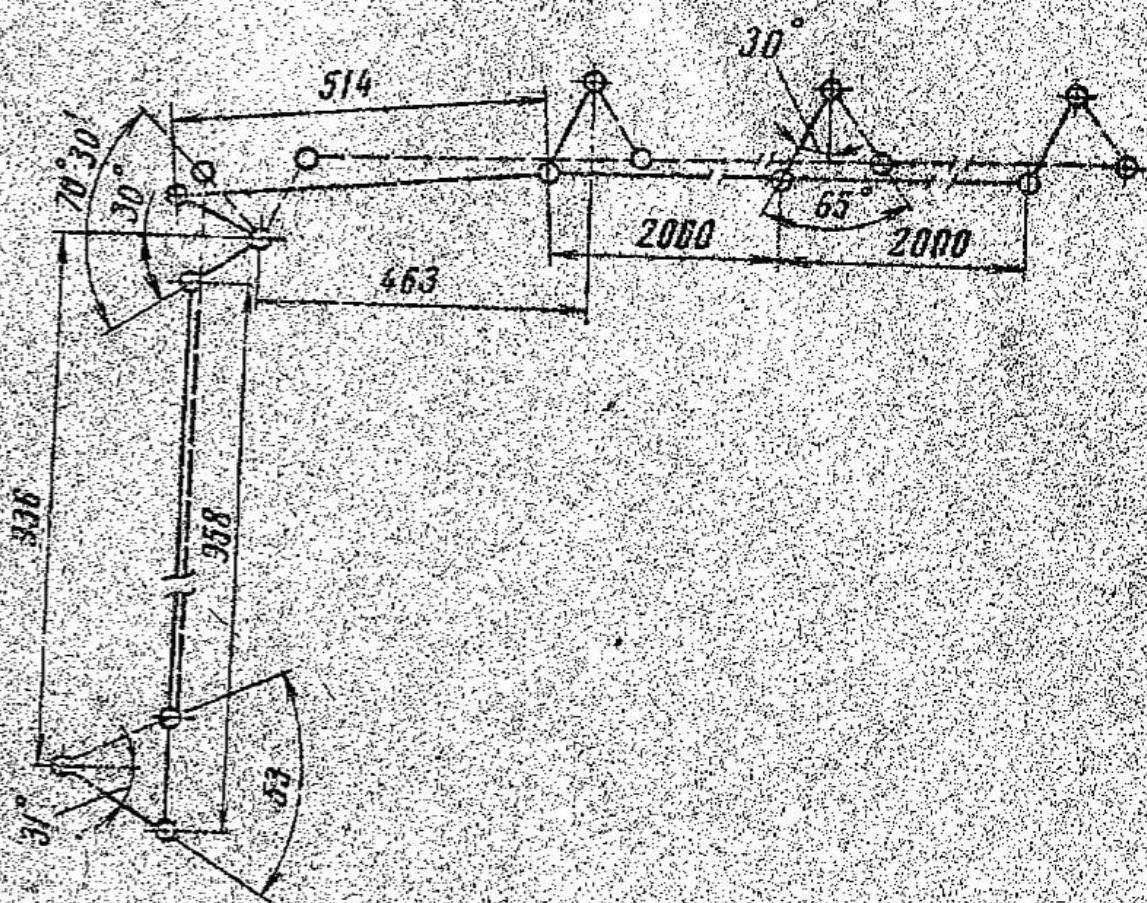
Кинематическая схема соединения механизма выключателя МКП-110М-1000/630-20 с приводом ШПЭ-33 (указанным углом поворота соответствует зазор 20...25 мм между штоком и роликом привода в отключенном положении)
